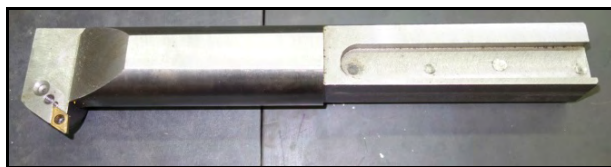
Универсальная державка под сменные пластины для изготовления всех типов моделей
